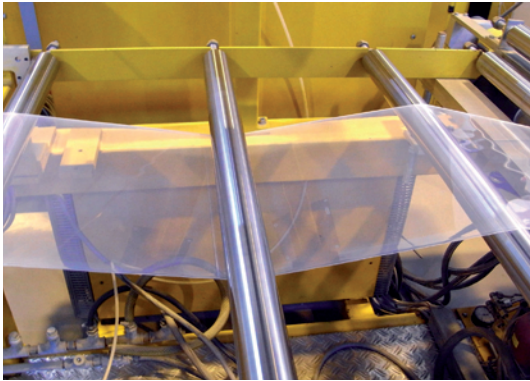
Paso del film por rodillos metálicos durante el proceso de extrusión y bobinado.
